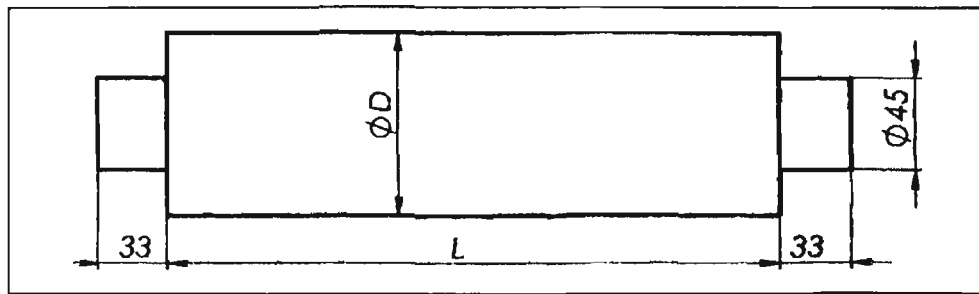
Габаритные и установочные размеры патрона высоковольтного предохранителя серии ПКТ- VV
